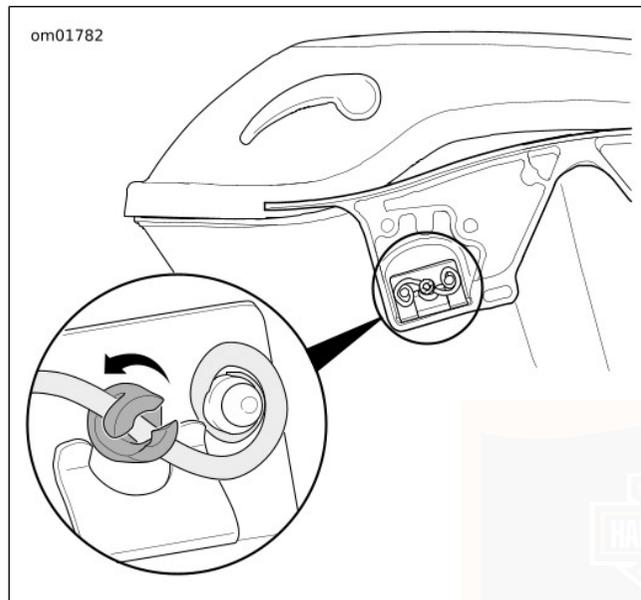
Installazione dei prigionieri di montaggio (vista in sezione)
